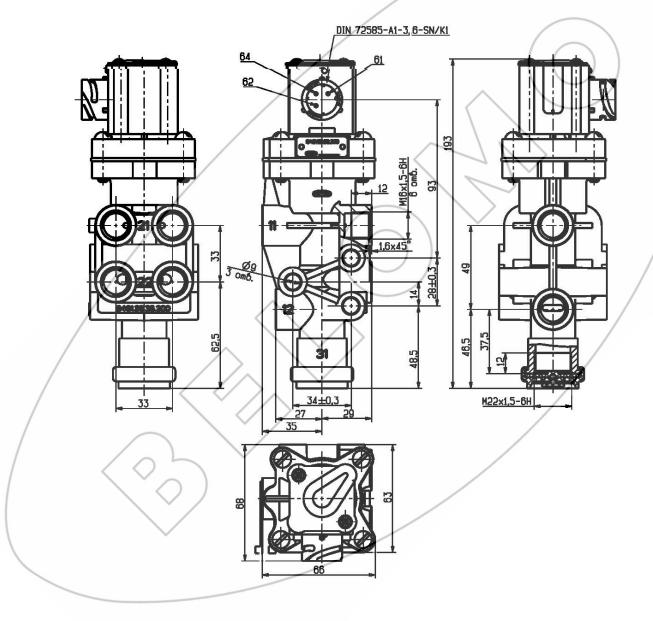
Габаритные и присоединительные размеры клапана.
